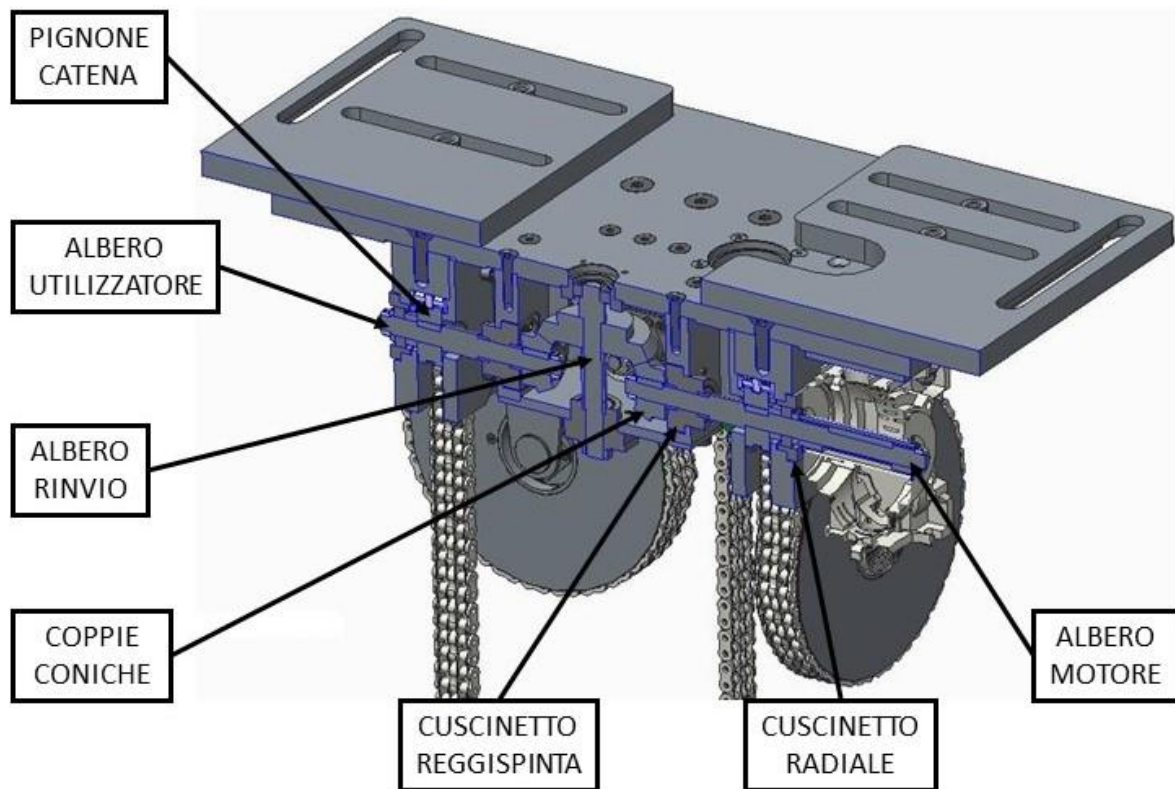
Sezione 3D del sistema di sollevamento.
